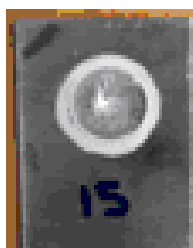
Внешний вид сварных точек при сварке АМГ-3 образцов толщиной (2+2) мм
